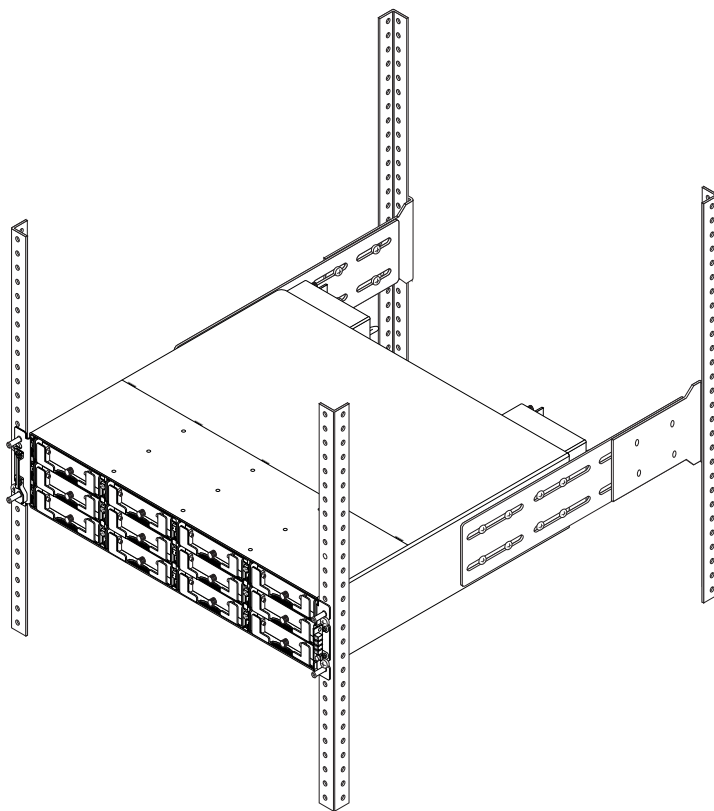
Baie de disques d'armoire montée en bâti sans les pattes et les panneaux frontaux du châssis, après installation
